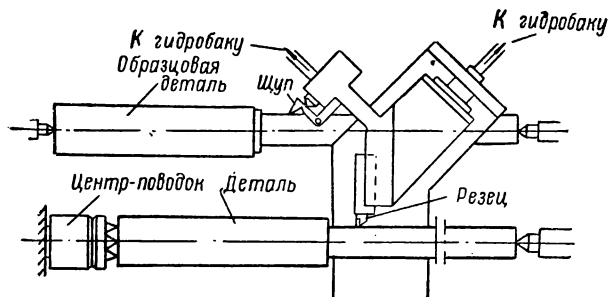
Схема обработки двухступенчатого валика с помощью гидросуппорта КСТ-1.
